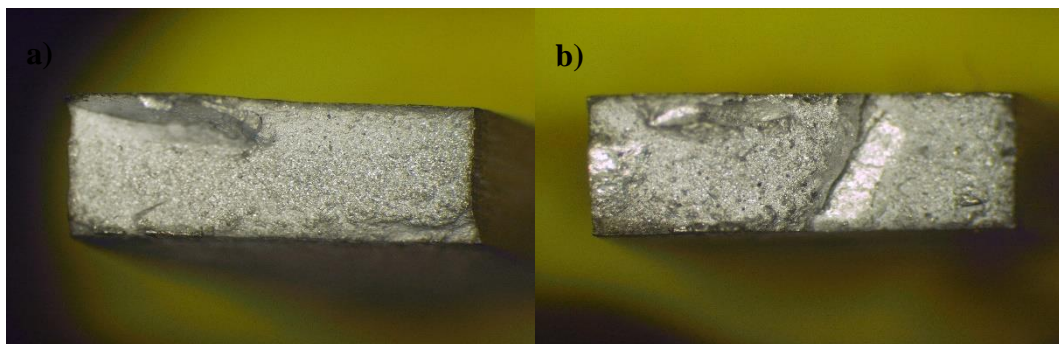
Superfícies de fratura dos provetes 6A (a) e 6B (b)
